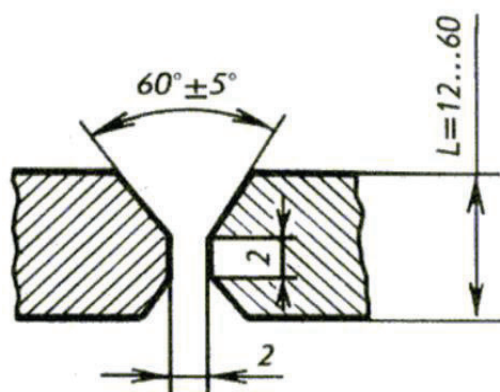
Підготовка кромки металу товщиною 12-60 мм до зварювання
